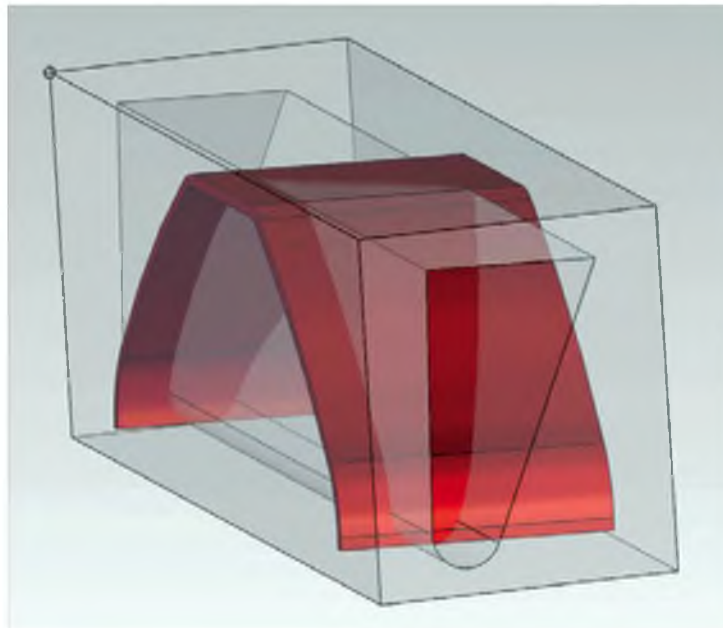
Fahrwerkrohling mit Beschnittwerkzeug
